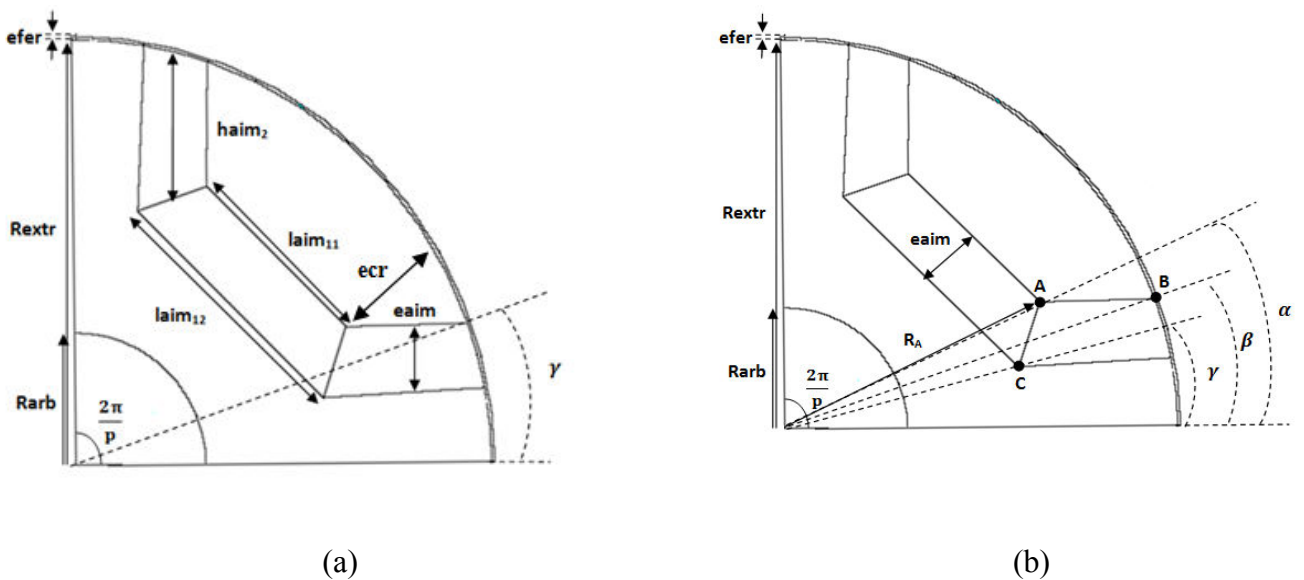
Dimensions géométriques du rotor de la machine étudiée
